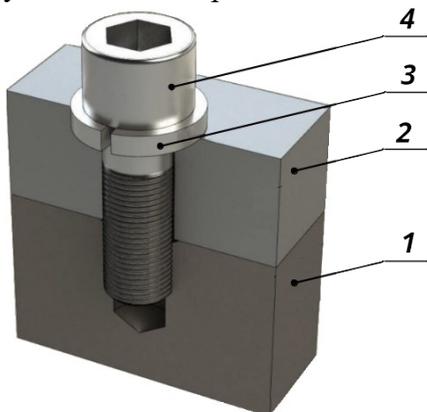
Соединение деталей винтом: 1 и 2 – соединяемые детали, 3 – шайба, 4 – винт
